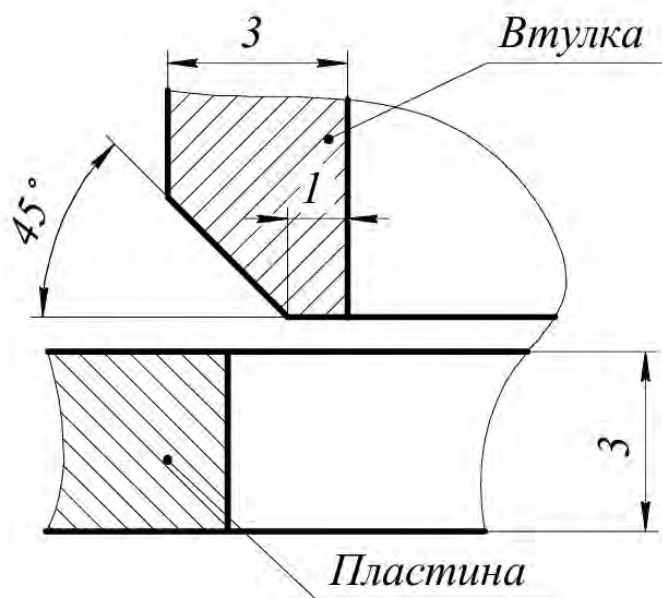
Коническая форма рельефа на торце втулки при контактной рельефной сварке
